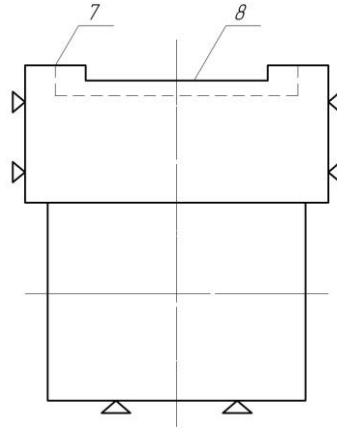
Схема закріплення заготовки (сухар) в лещатах пневматичних
